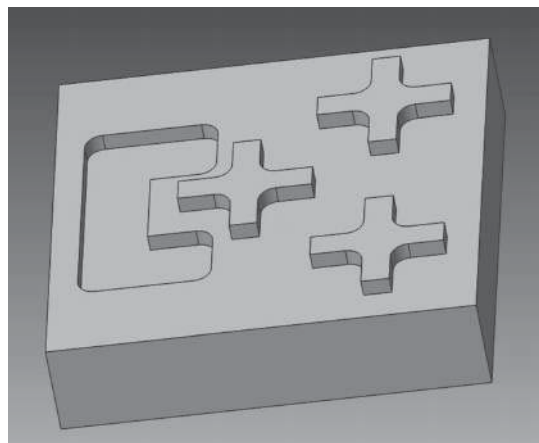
3D модель детали для проверки работы цикла измерения заготовки
